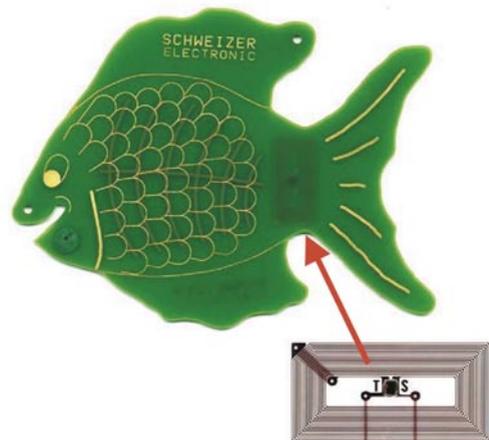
Schweizer iBoard Test-Vehikel und Schweizer iFish
